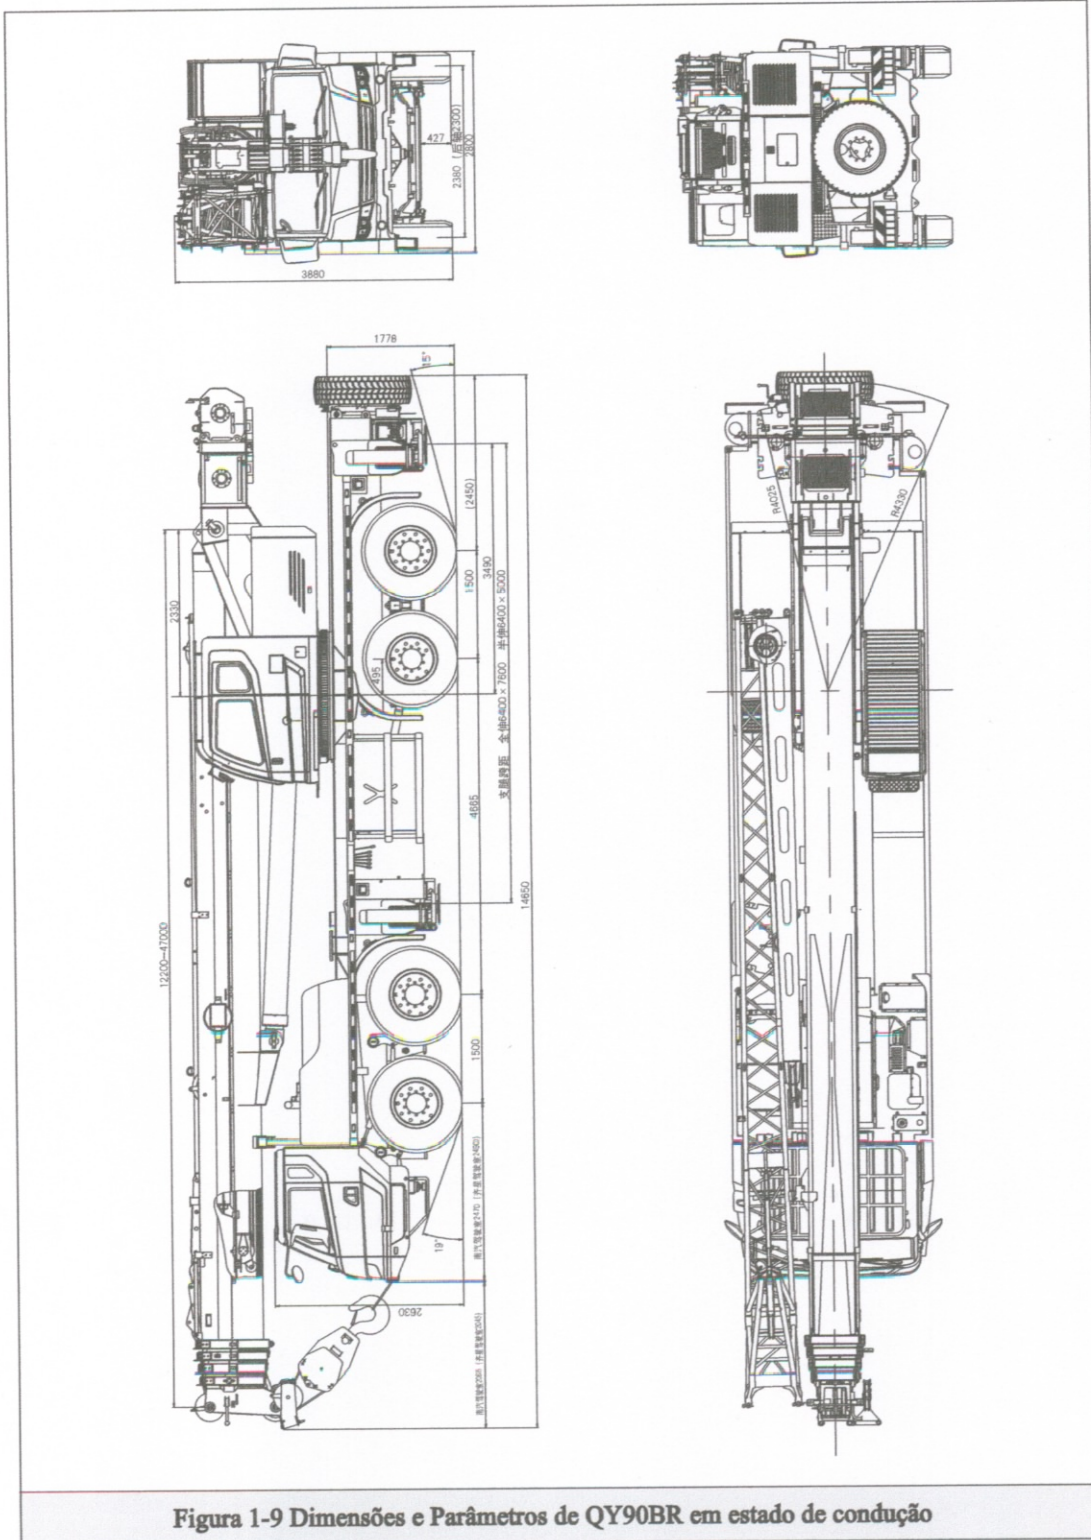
Dimensões e Parâmetros de QY90BR em estado de condução
